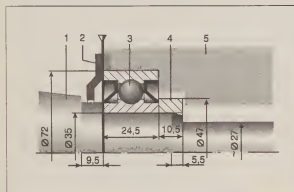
Конструкция опоры полуоси "Форда-Таунус": 1 — полуось; 2 — крышка; 3 — подшипник; 4 — запорное кольцо; 5 — балка.
